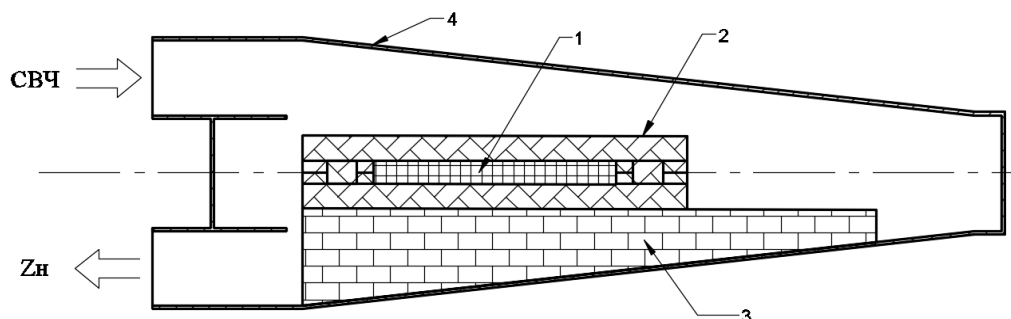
Схематичное изображение СВЧ рабочей камеры: 1 – керамическая заготовка; 2 – огнеупорная форма; 3 – теплоизоляция; 4 – корпус камеры; СВЧ – ввод СВЧ энергии; Z_n – балластная нагрузка
